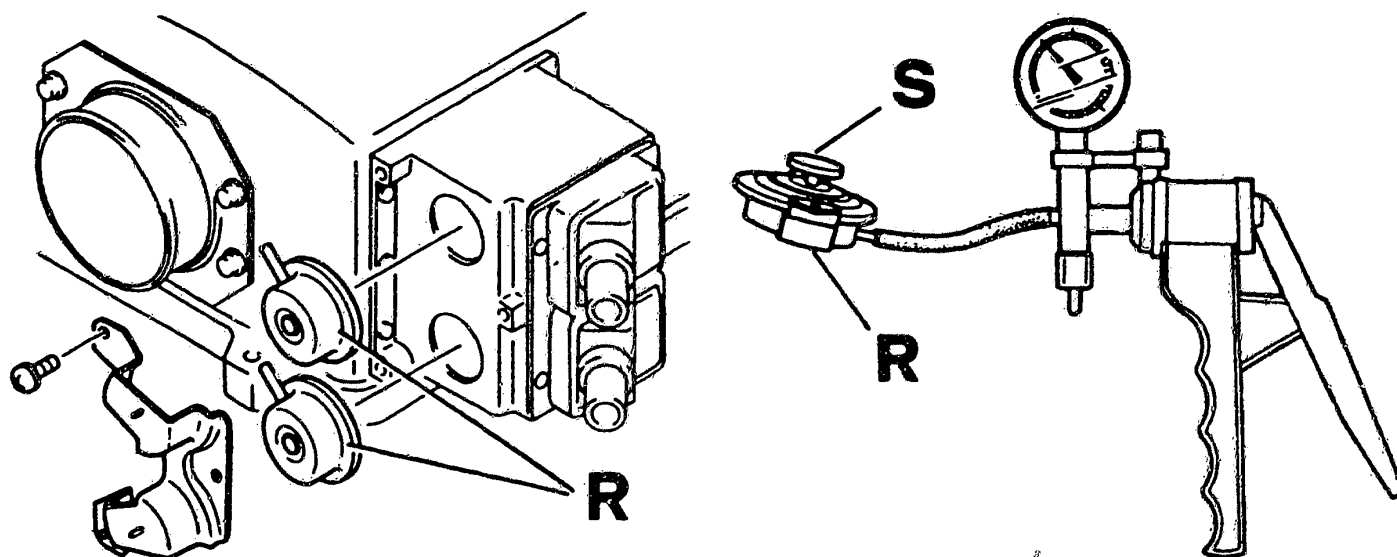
Die ausgebauten Abschaltventile R für die Luftzufuhr hinter die Auslassventile lassen sich mit der Unterdruck-Handpumpe prüfen. Der Stößel S muss sich bei einem Unterdruck von 0,09...0,12 bar (70...90 mm Hg) zu bewegen beginnen.
